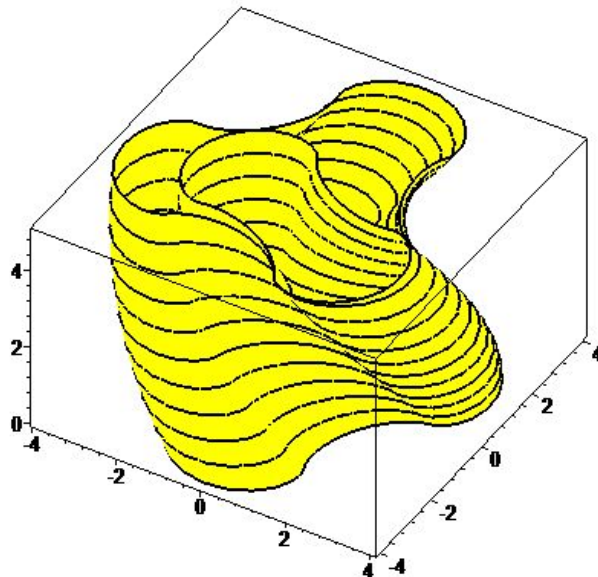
Зачеплення робочих поверхонь корпусу і ротора
